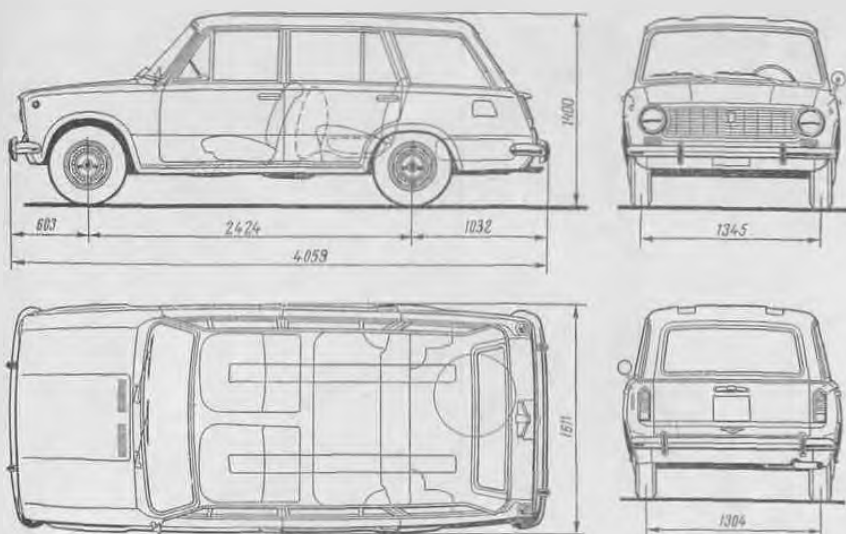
Габаритные размеры автомобиля «Жигули» (ВАЗ-2102) с кузовом «универсал»
